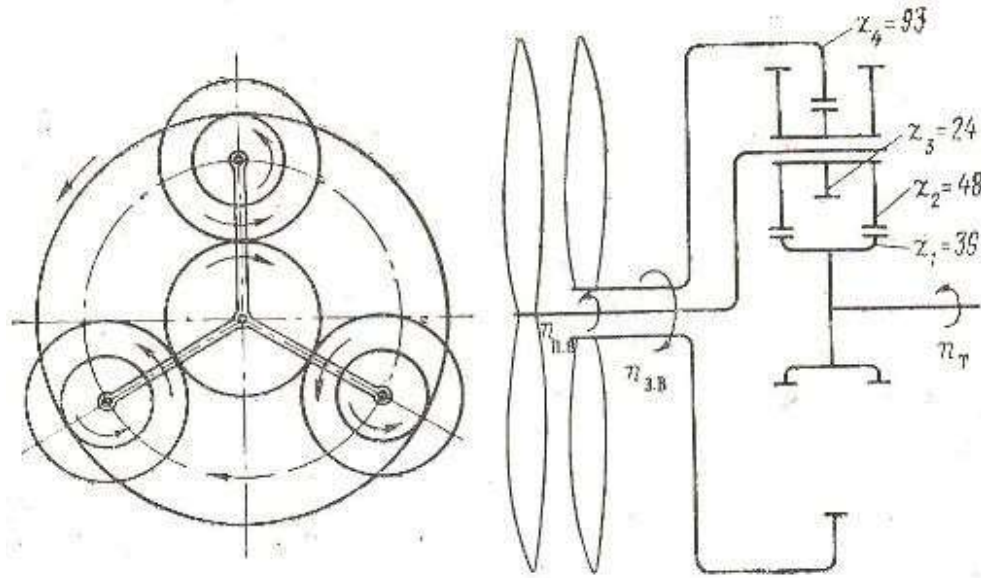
Кинематическая схема дифференциального редуктора двигателя НК-12
